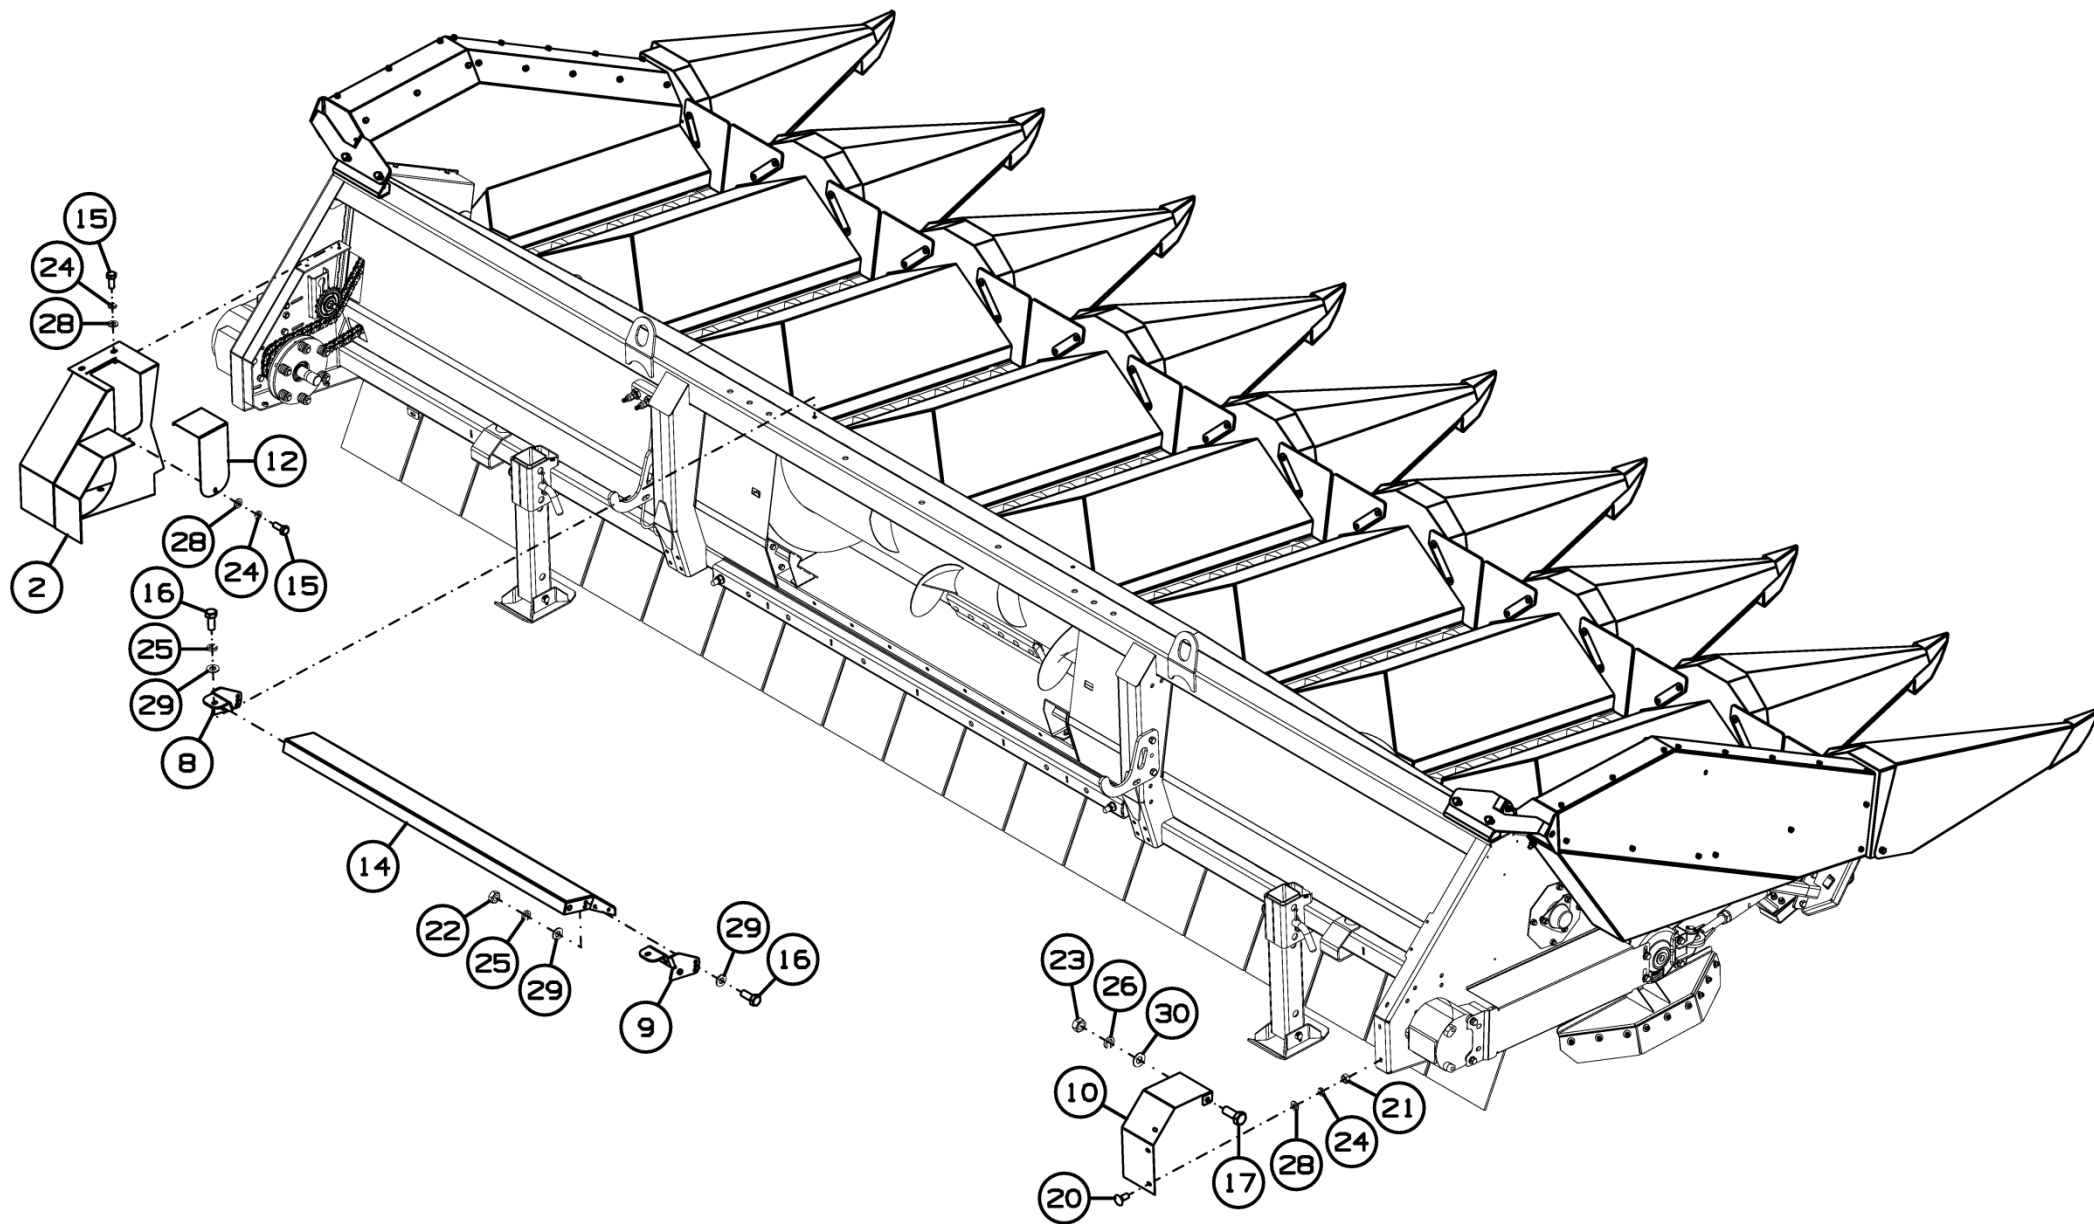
Установка капотов ППК-870.01.11.000А
